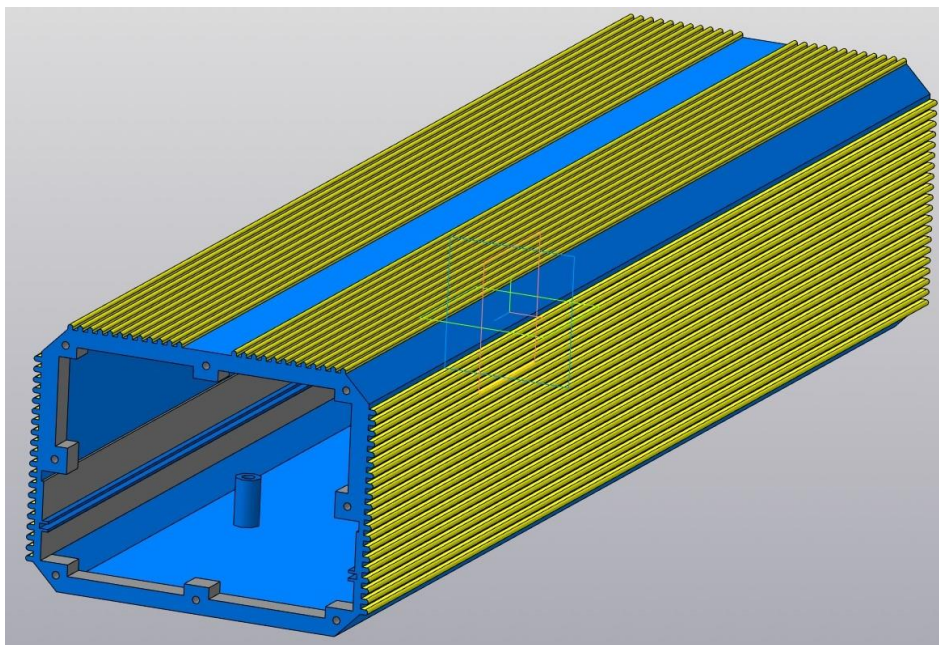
Створення ребер охолодження на бокових та верхніх стінках корпусу проєктованого інвертора напруги
